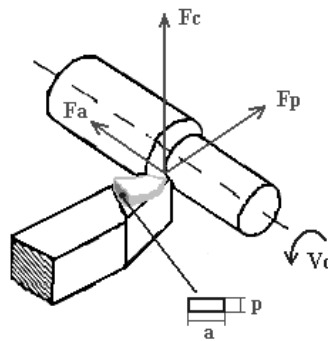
Fuerzas que ejerce la herramienta sobre la pieza
